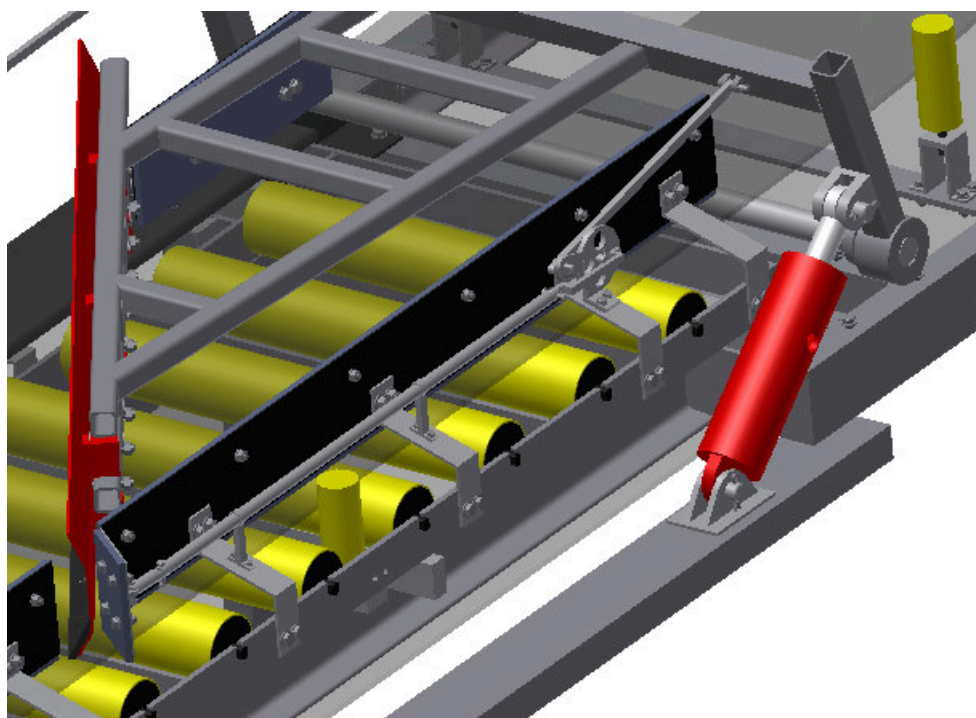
Schéma polohy mechanismu při otevřené bočnici na straně hydraulického pístu – pohled shora
